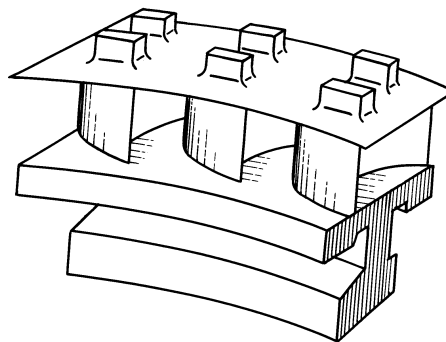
Сварной пакет из трех лопаток для регулирующей ступени
